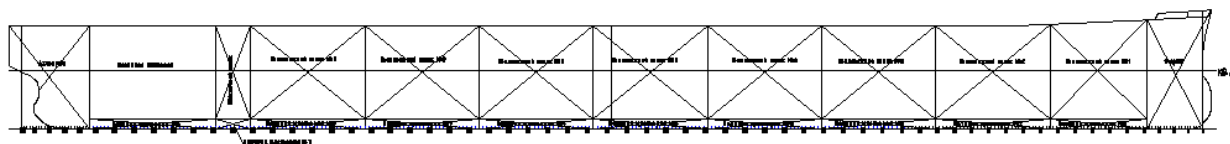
Схема повздовжнього перерізу корпусу судна з розділенням на відсіки
